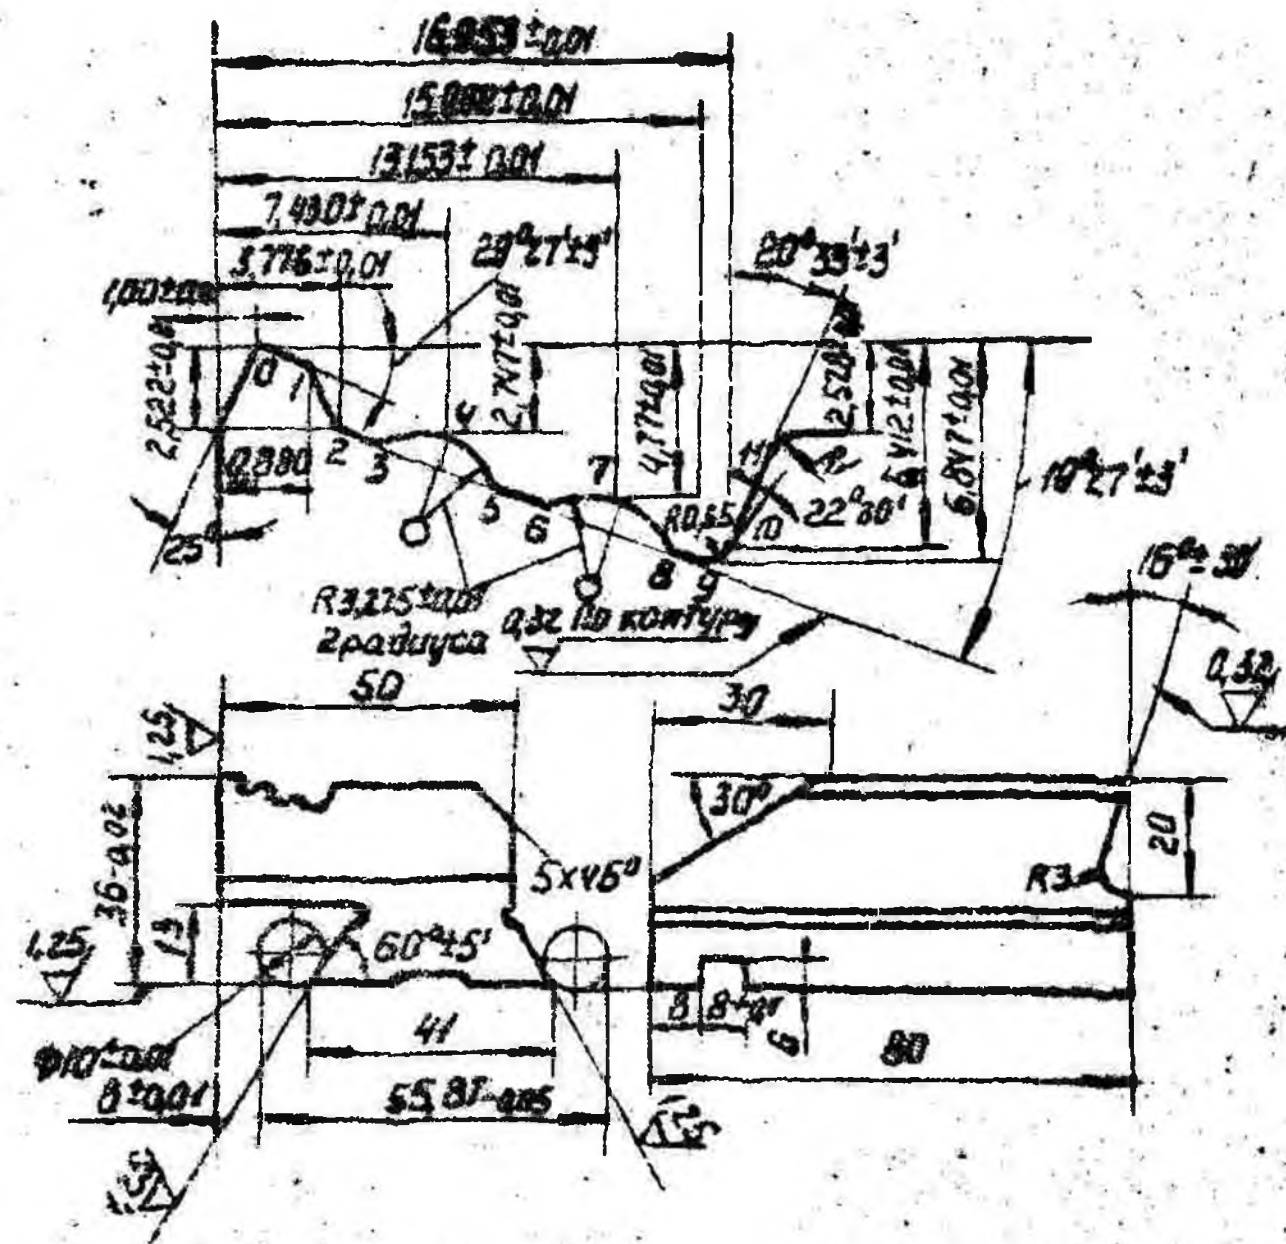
Чертеж призматического фасонного резца для обработки кольца I204
